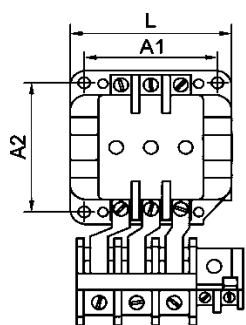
Пускатель нереверсивный ПМЕ-200. Степень защиты - IP00
